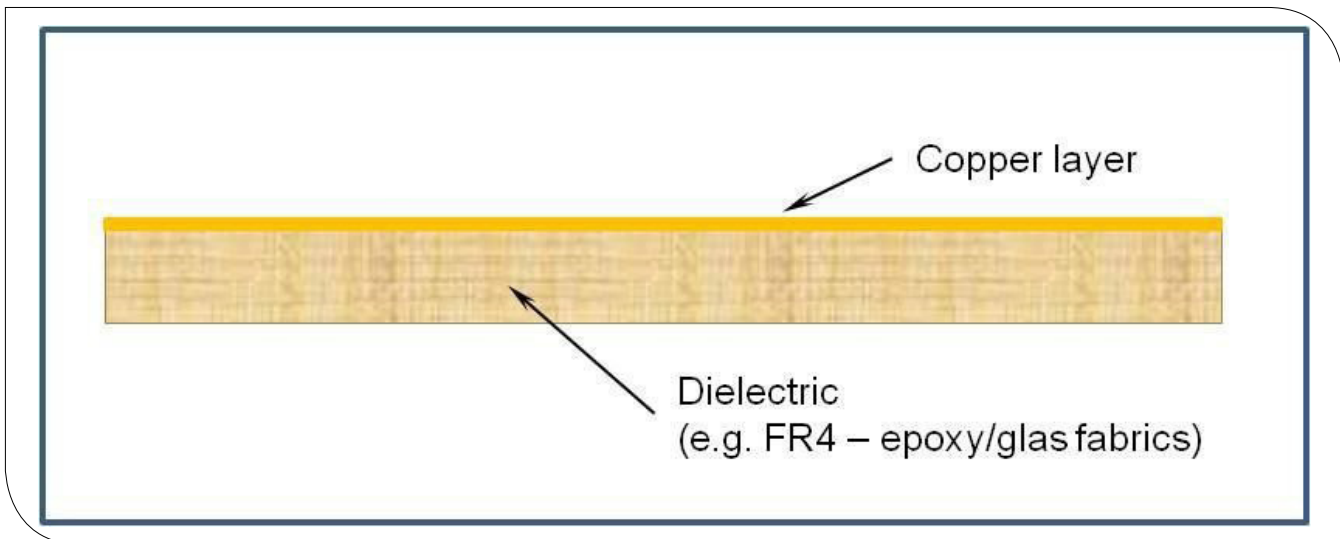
Rappresentazione schematica di un lato di un PCB FR4 (Fonte: Osram)
